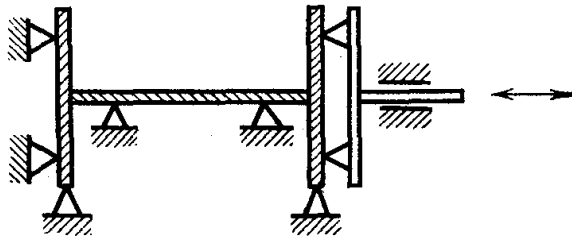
Схема кондуктора для сборки двутавровых балок
